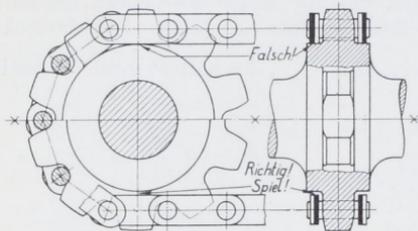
Richtige und falsche Ausbildung der Kettenräder.
